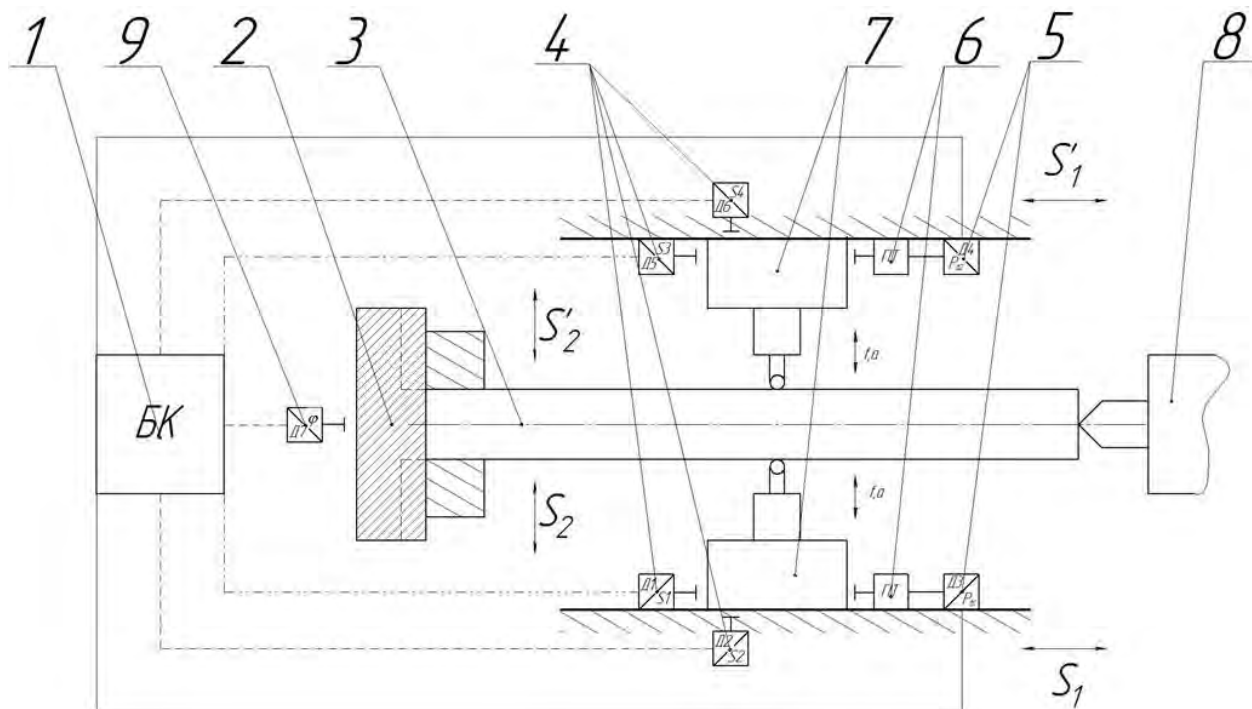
Принципова конструктивна схема адаптивної системи для поверхневого деформаційного зміцнення на базі гідроімпульсного приводу
